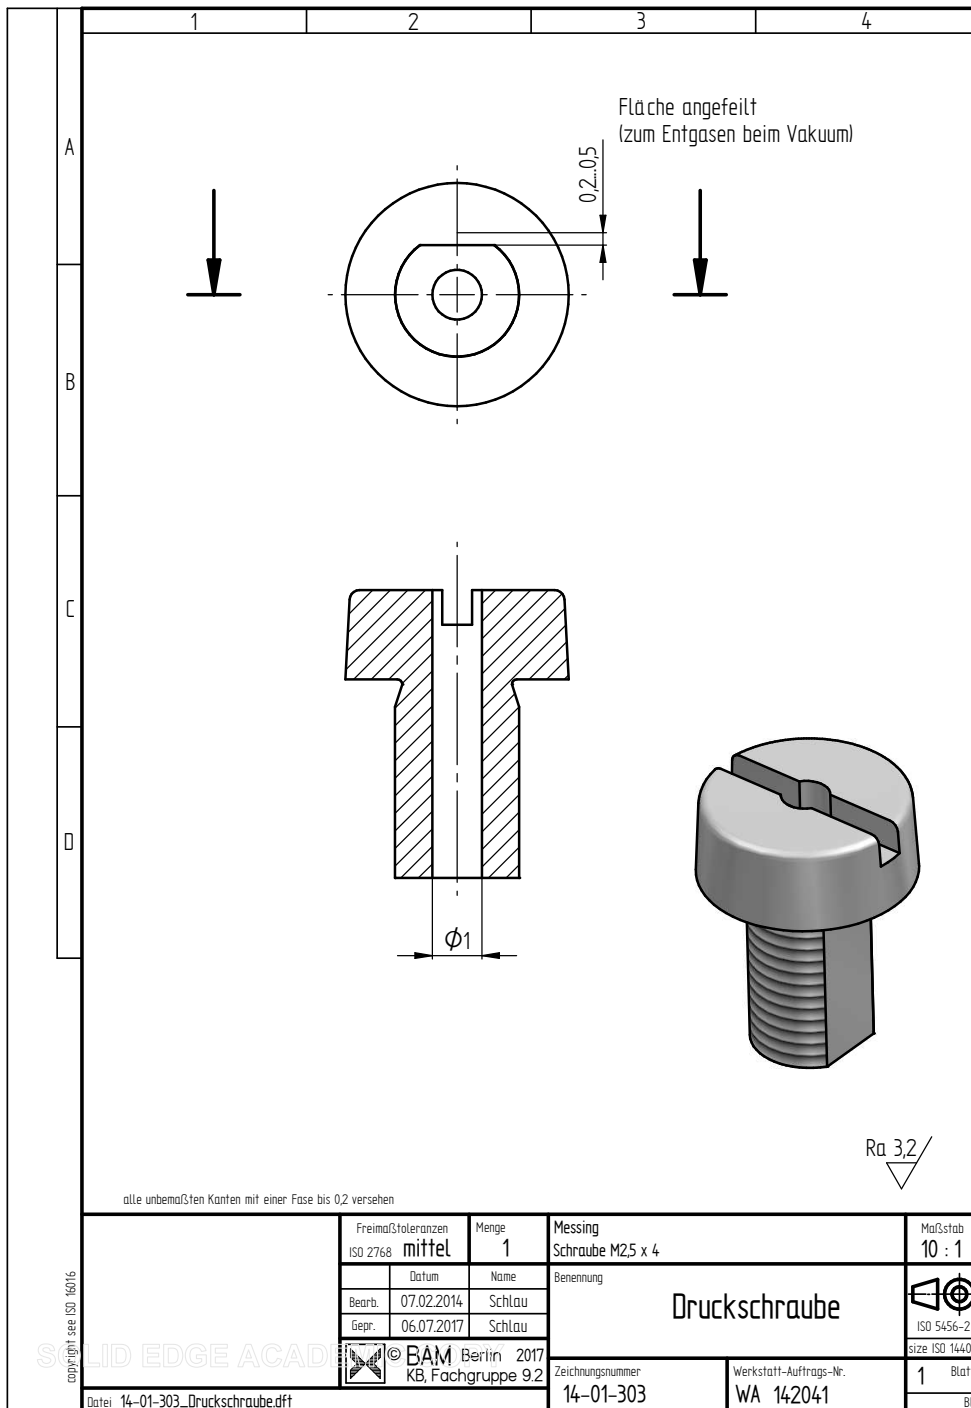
Die Druckschraube des Vakuumprobenhalters.
